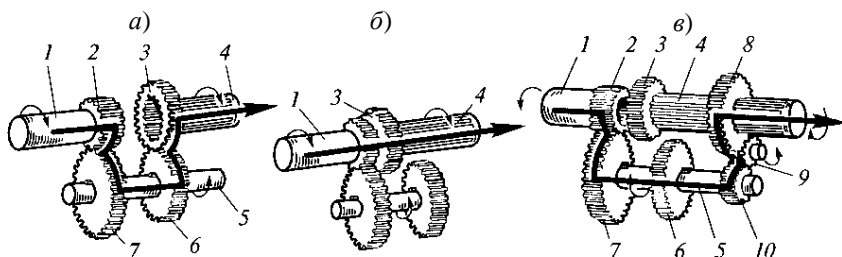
Схема работы трехвальной коробки передач:
